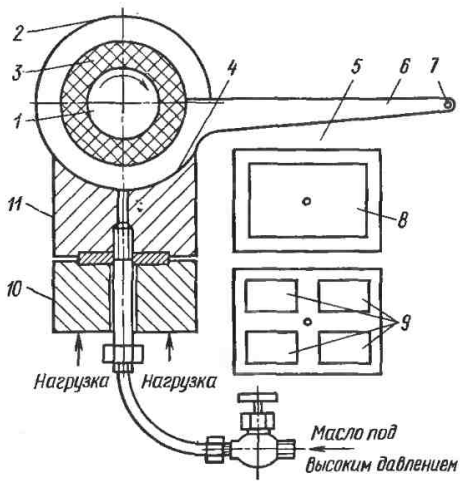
Гидростатическая смазка устройства для изучения подшипников скольжения:
